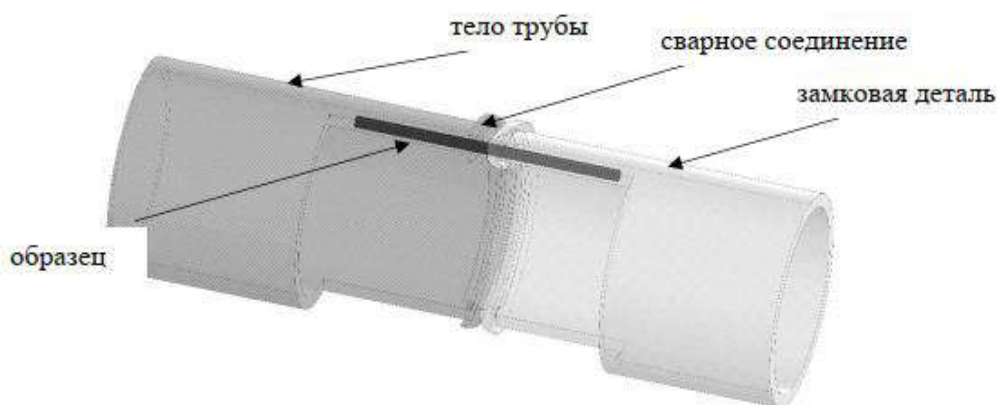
Схема вырезки образца со сварным соединением для испытаний на усталость
